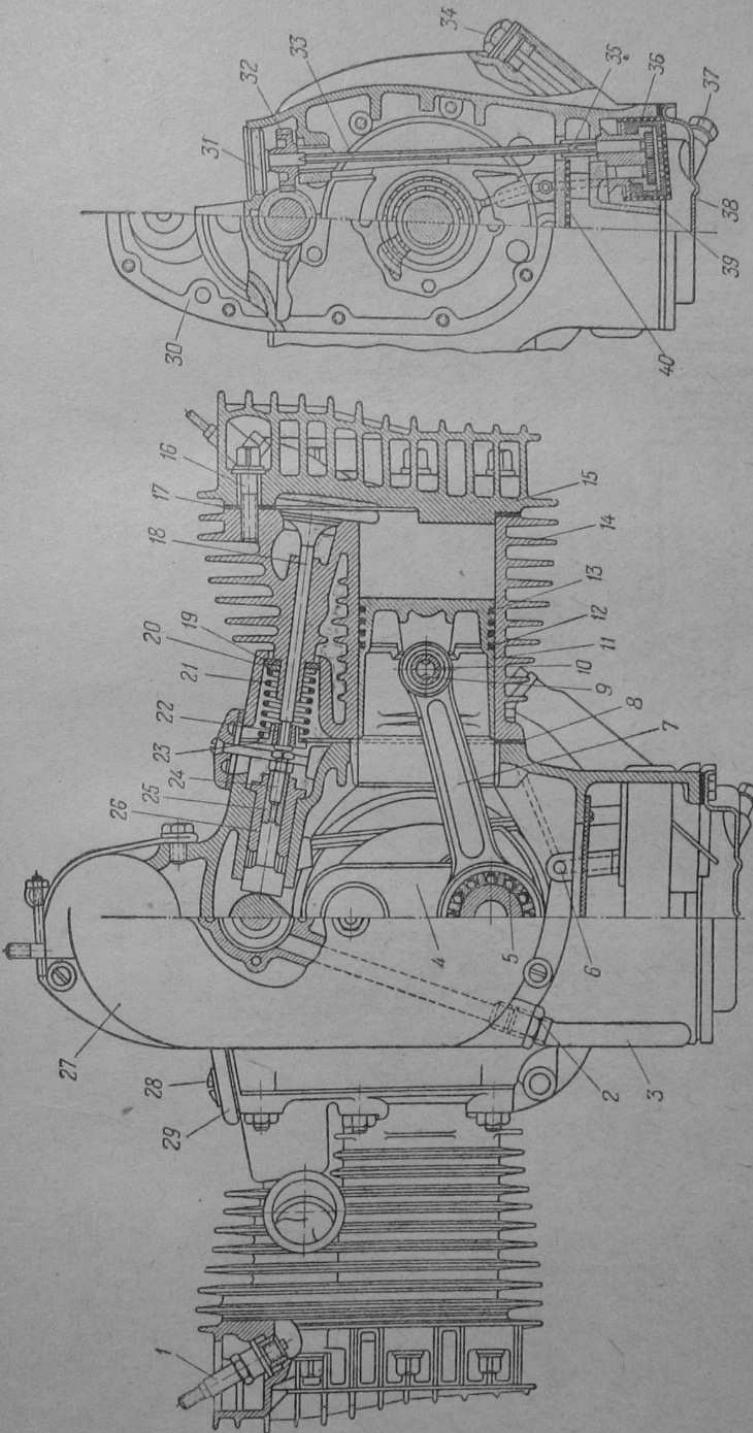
Двигатель мотоцикла М-72. Поперечный разрез:
